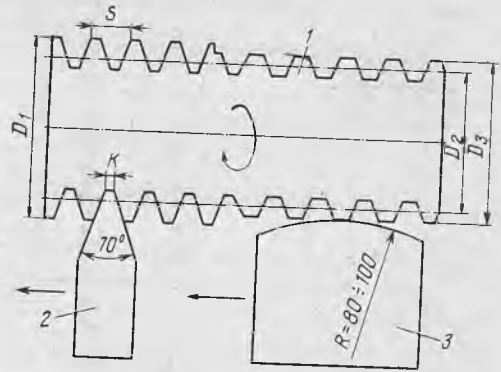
Схема накатывания и сглаживания деформированной поверхности детали: 1 — восстанавливаемая деталь; 2 — инструмент для высадки; 3 — гладилка; D_1 — диаметр детали после высадки; D_2 — диаметр изношенной детали; D_3 — диаметр детали после сглаживания; S — шаг высадки; K — ширина вершины инструмента для высадки
